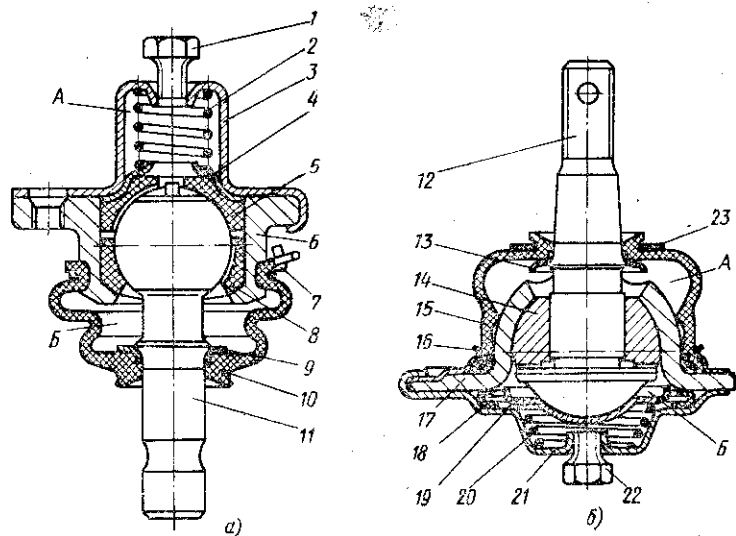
Шаровый шарнир и опора стойки передней подвески:
